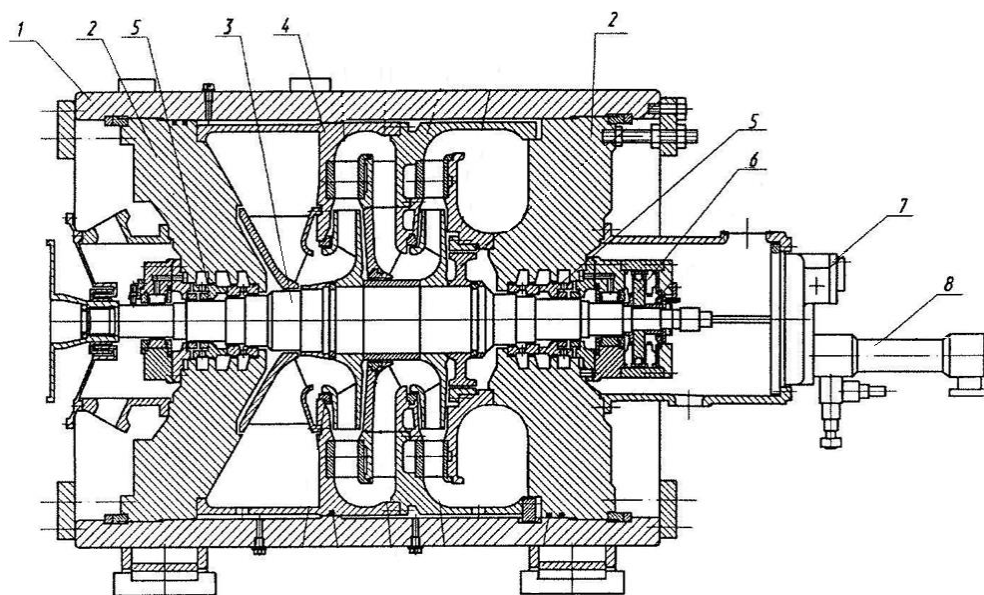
Відцентровий компресор НЦ-16/76-1,44 потужністю 16 МВт агрегату ГПА-Ц-16/76-1,44:1 – корпус; 2 – кришки корпуса; 3 – ротор; 4 – статорні елементи; 5 – кінцеві ущільнення ротора; 6 – мастильні підшипники; 7 – насос системи змащення; 8 – мастильний насос системи ущільнення
